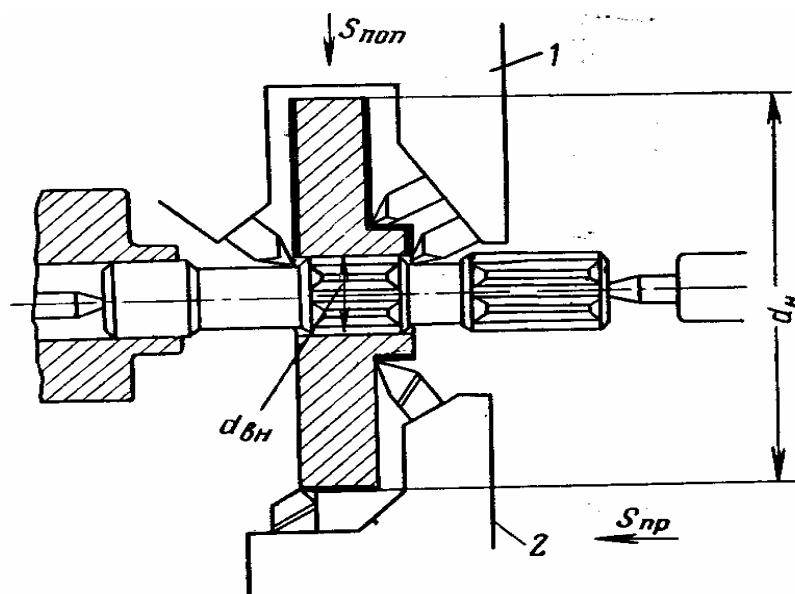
Схема обработки заготовки цилиндрического зубчатого колеса
